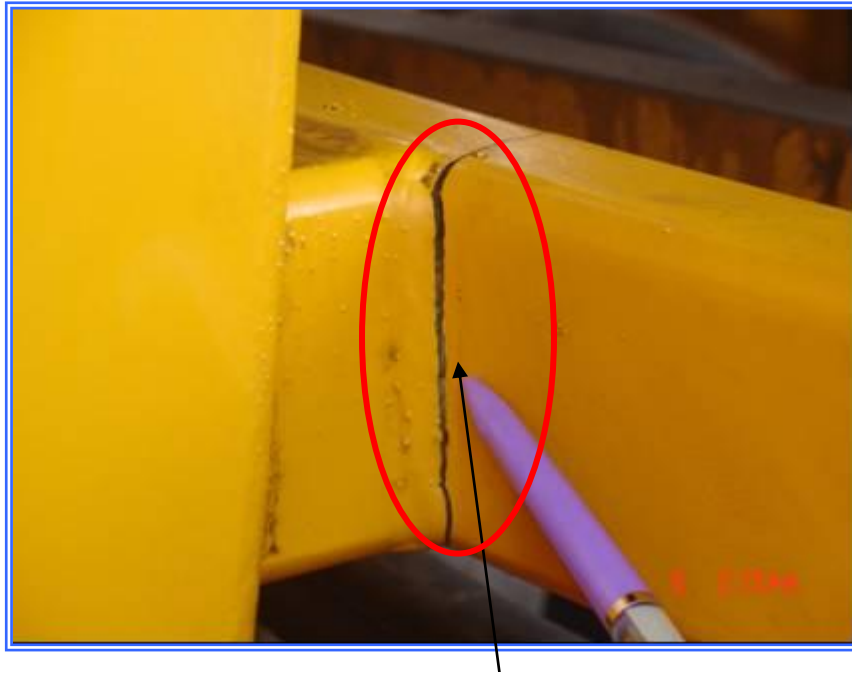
, Fisura en la viga secundaria que soporta las mangueras hidráulicas del conjunto de bateo.
